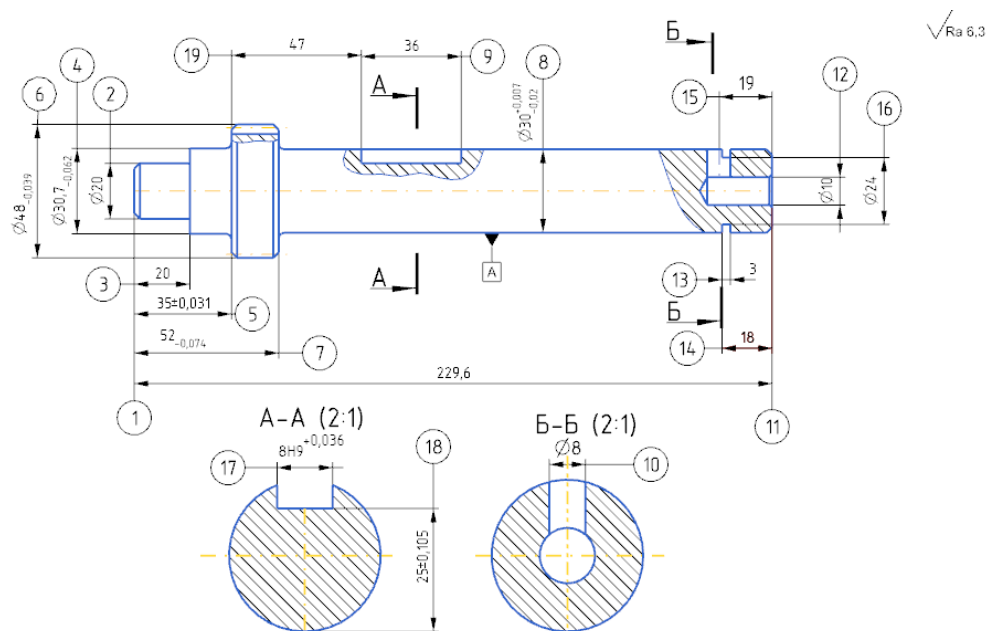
Конструкторсько-технологічні елементи деталі
